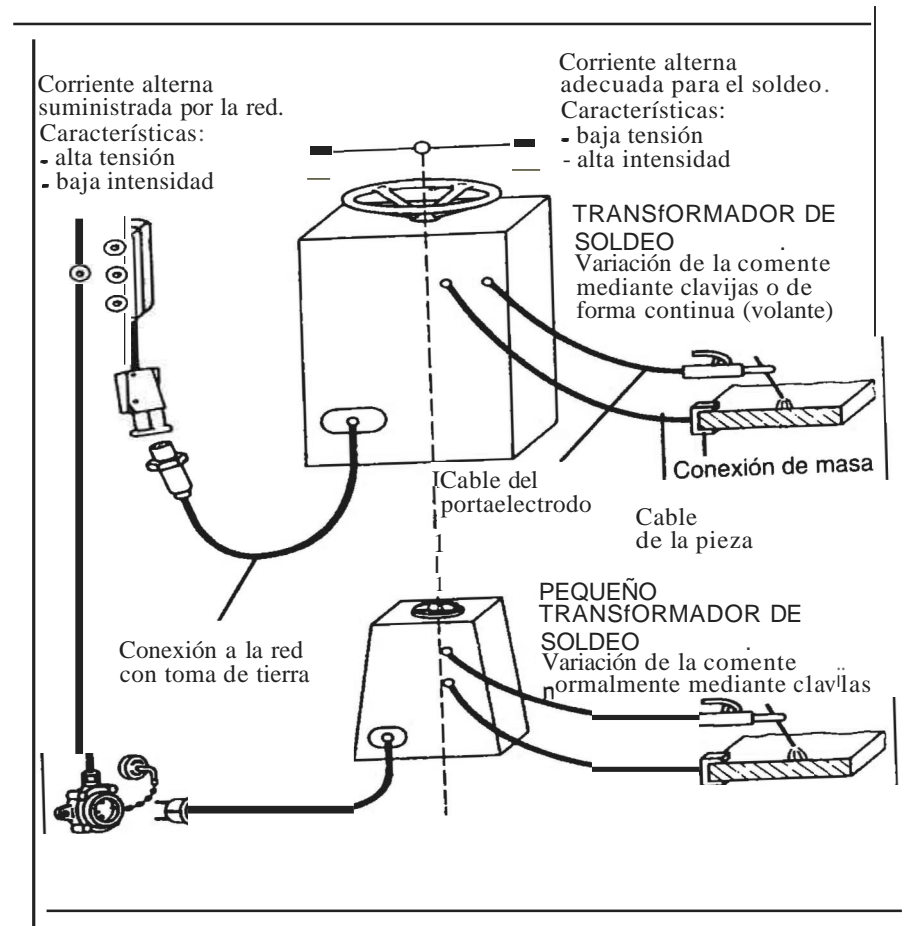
TRANSFORMADORES DE SOLDEO
